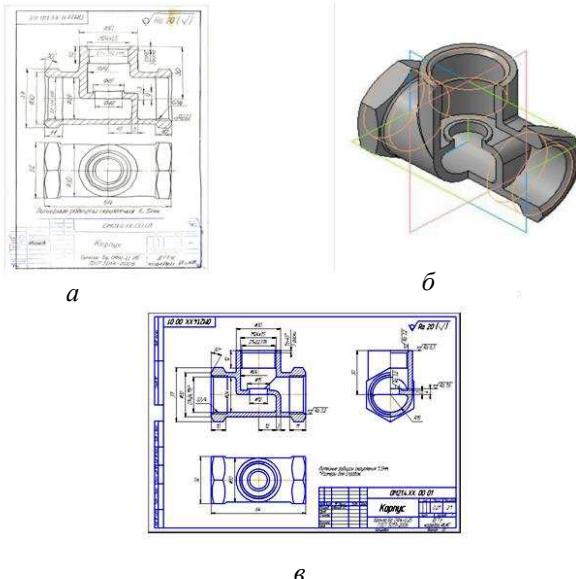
Деталь «Корпус» – этапы работы: *а* – отсканированный эскиз детали; *б* – твердотельная 3D-модель; *в* – компьютерный ассоциативный чертеж
